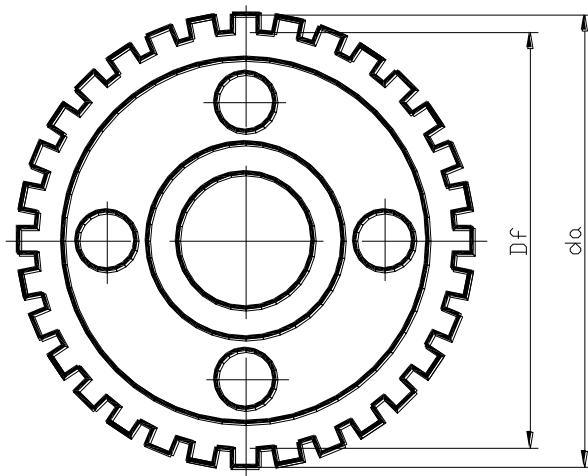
Конструкція шківа зубчатопасової передачі.
